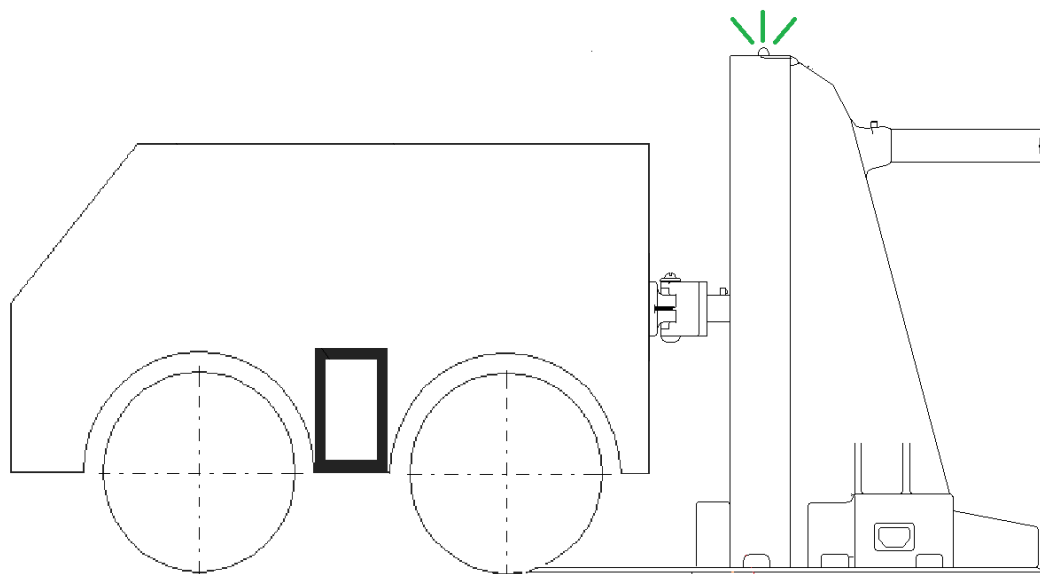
Stav dobíjecí stanice před spojením robota s dobíjecí základnou
